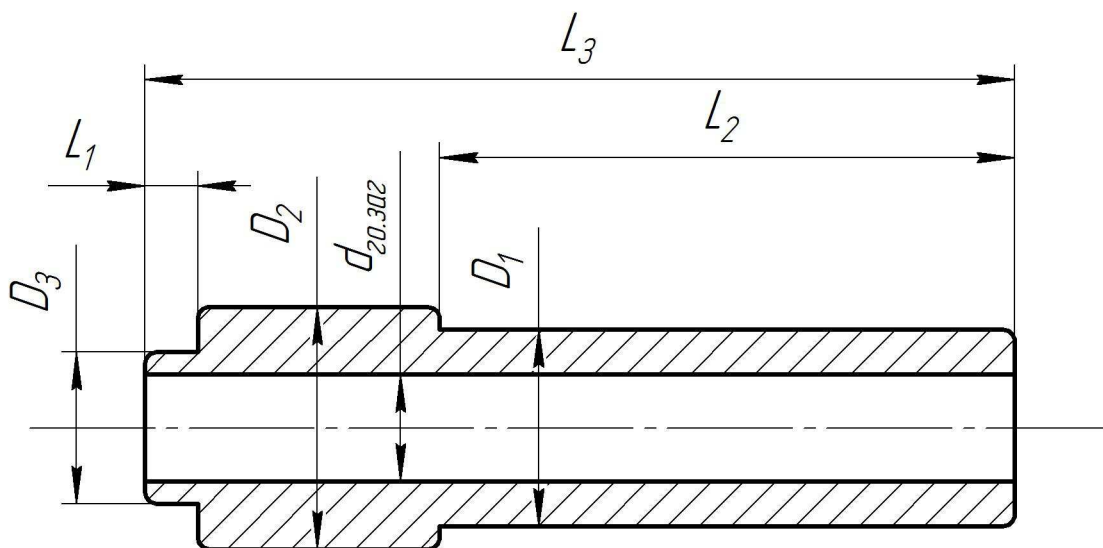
Вид заготовки при растачивании глубокого отверстия
